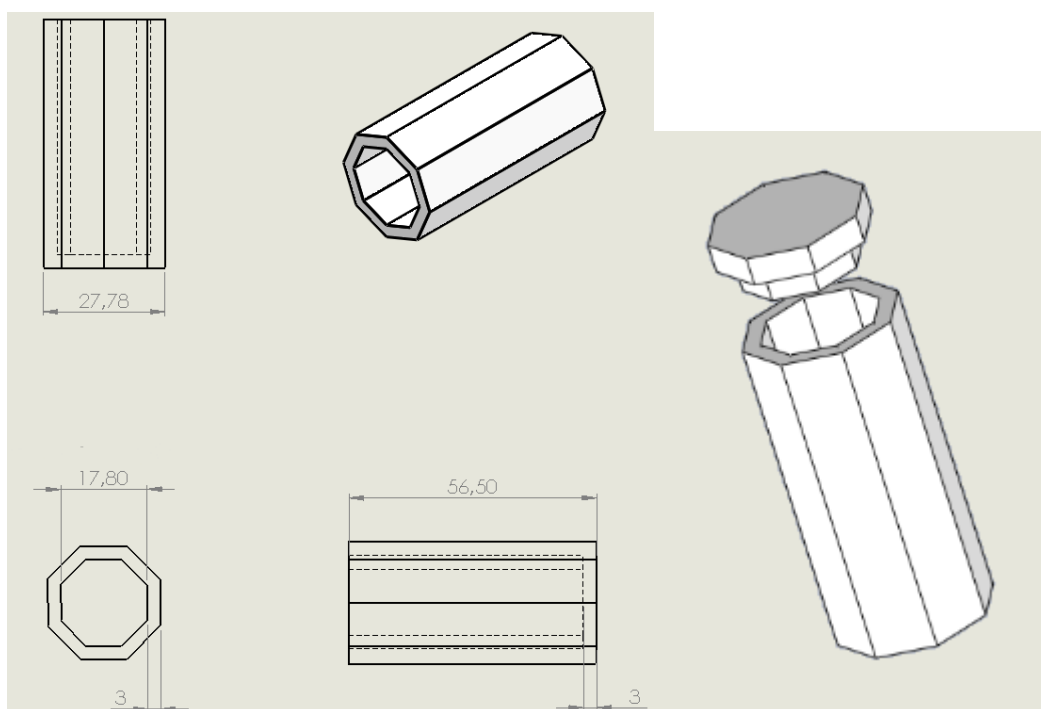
a) Vistas do projeto do tambor. b) Montagem do tambor com a tampa.
